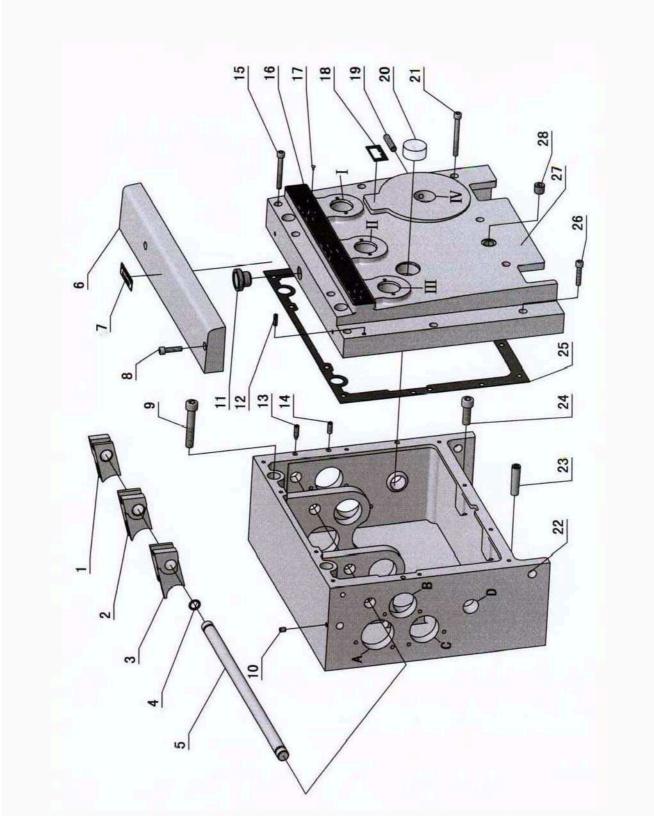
Vorschubgetriebe 1 von 4 - Headstock feed gear 1 of 4
